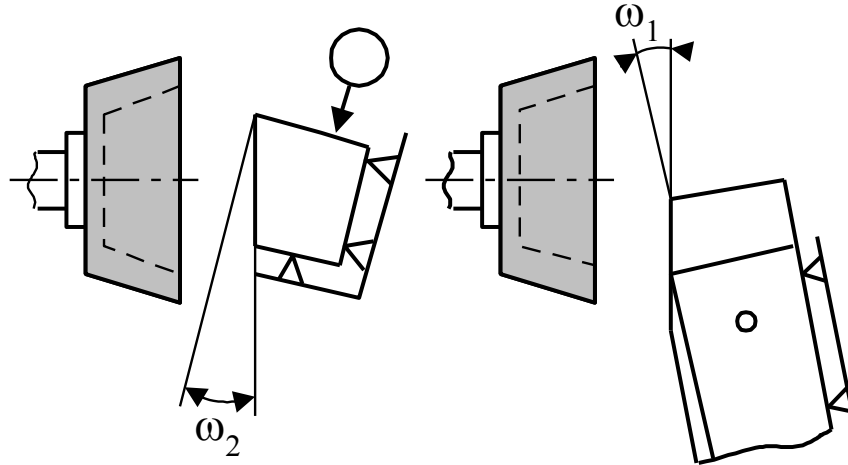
Установка державки резца при шлифовании опорной поверхности гнезда под пластинку на станке
